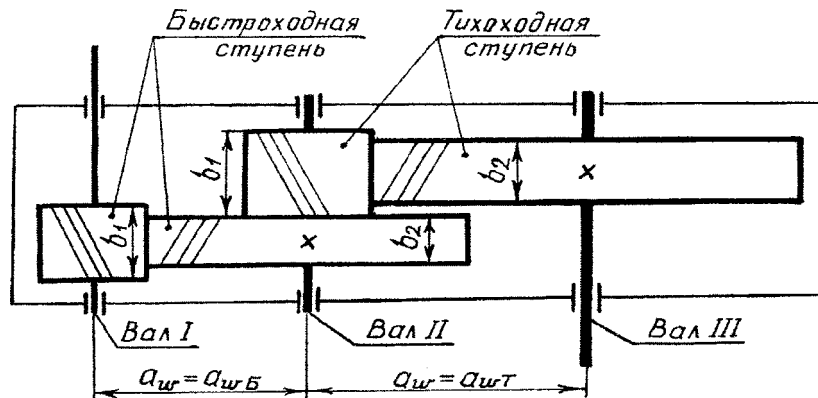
Кинематическая схема двухступенчатого цилиндрического косозубого горизонтального редуктора, выполненного по простой развернутой схеме
